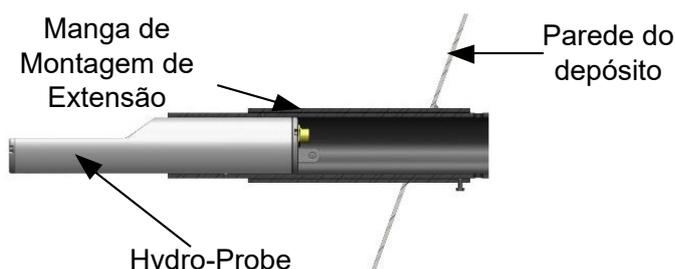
Hydro-Probe instalado numa Manga de Montagem de Extensão
